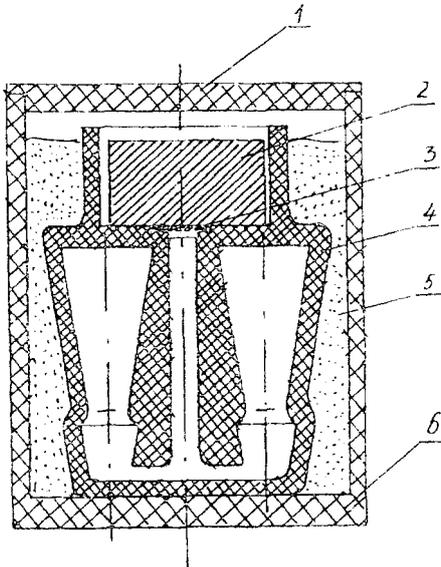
Форма для литья лопаток: 1 - графитовая крышка; 2 - шихтовая заготовка; 3 - никелевая фольга; 4 - керамическая оболочка формы; 5 графитовая засыпка; 6 - графитовая опока
